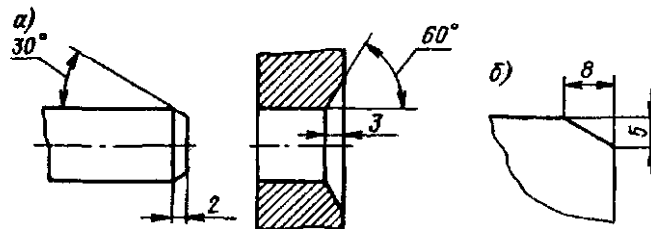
Нанесение размеров фасок под углами, отличными от 45°
